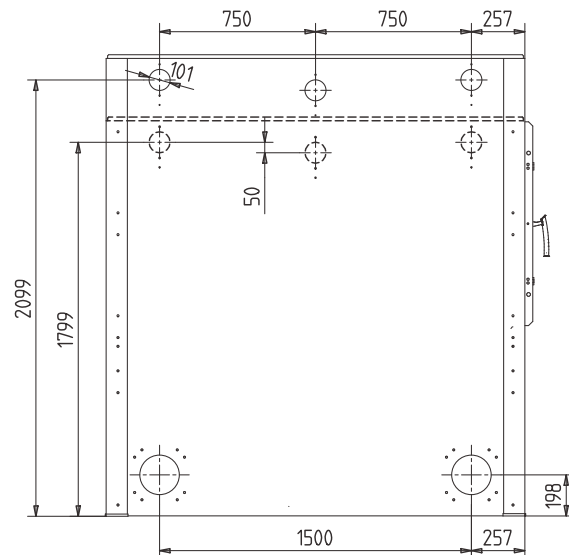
Stahlblech-Tanks mit Breite 2,0 m – Ansicht von links
